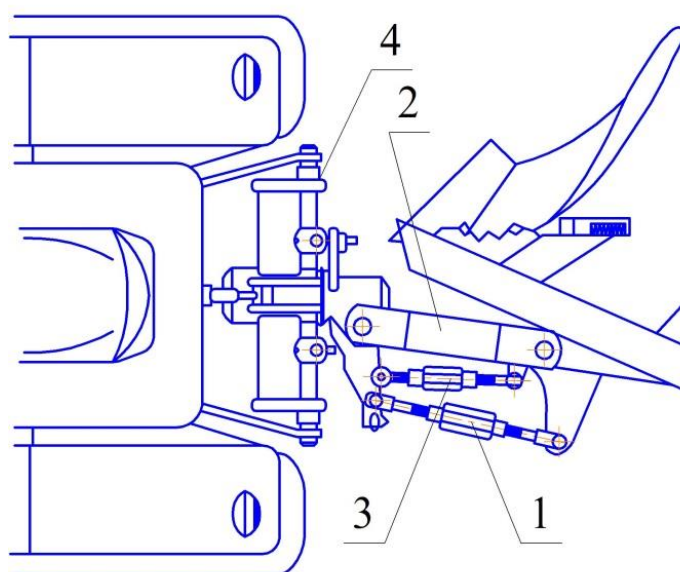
Схема механізмів регулювання лінії тяги та ширини захвату корпусів оборотних плугів:
